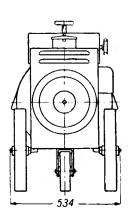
Massbild des Schweissumformers EW-21u
